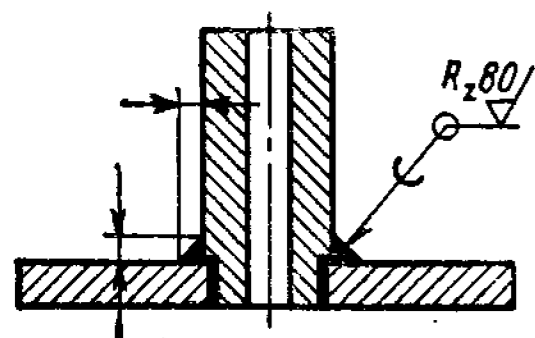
Указание шероховатости и размеров шва паяного соединения
